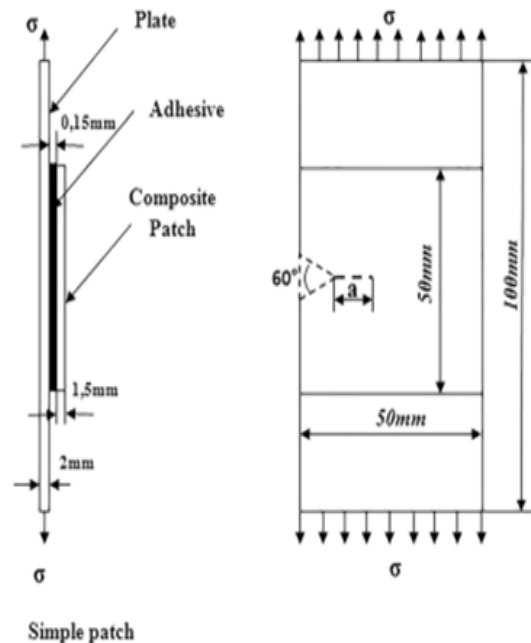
Modèle géométrique de l'assemblage (plaque d'aluminium, pièce composite et adhésif
